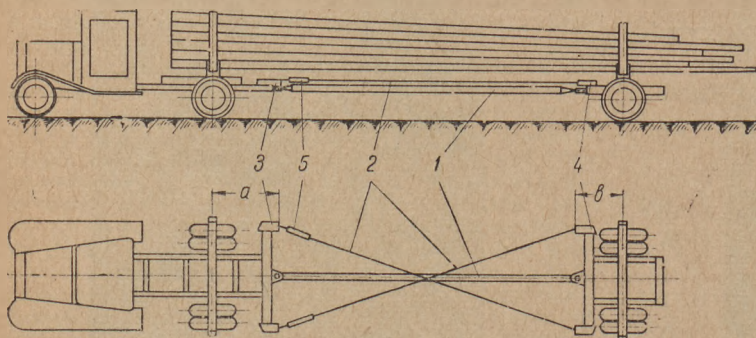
Автопоезд, оборудованный новой сцепкой:
